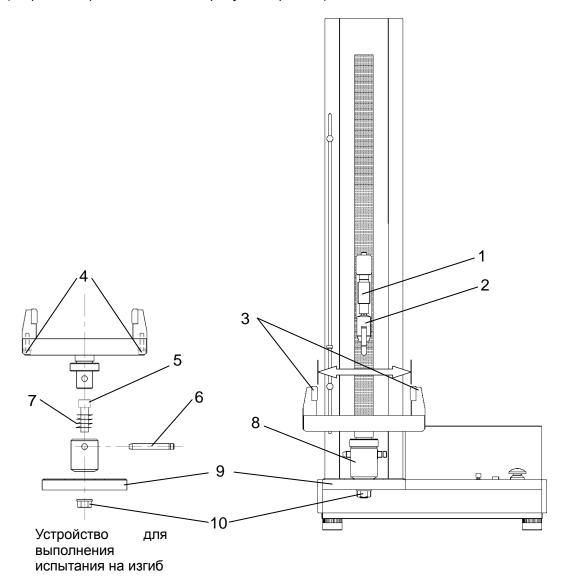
Установка приспособлений для проведения испытания на изгиб.
